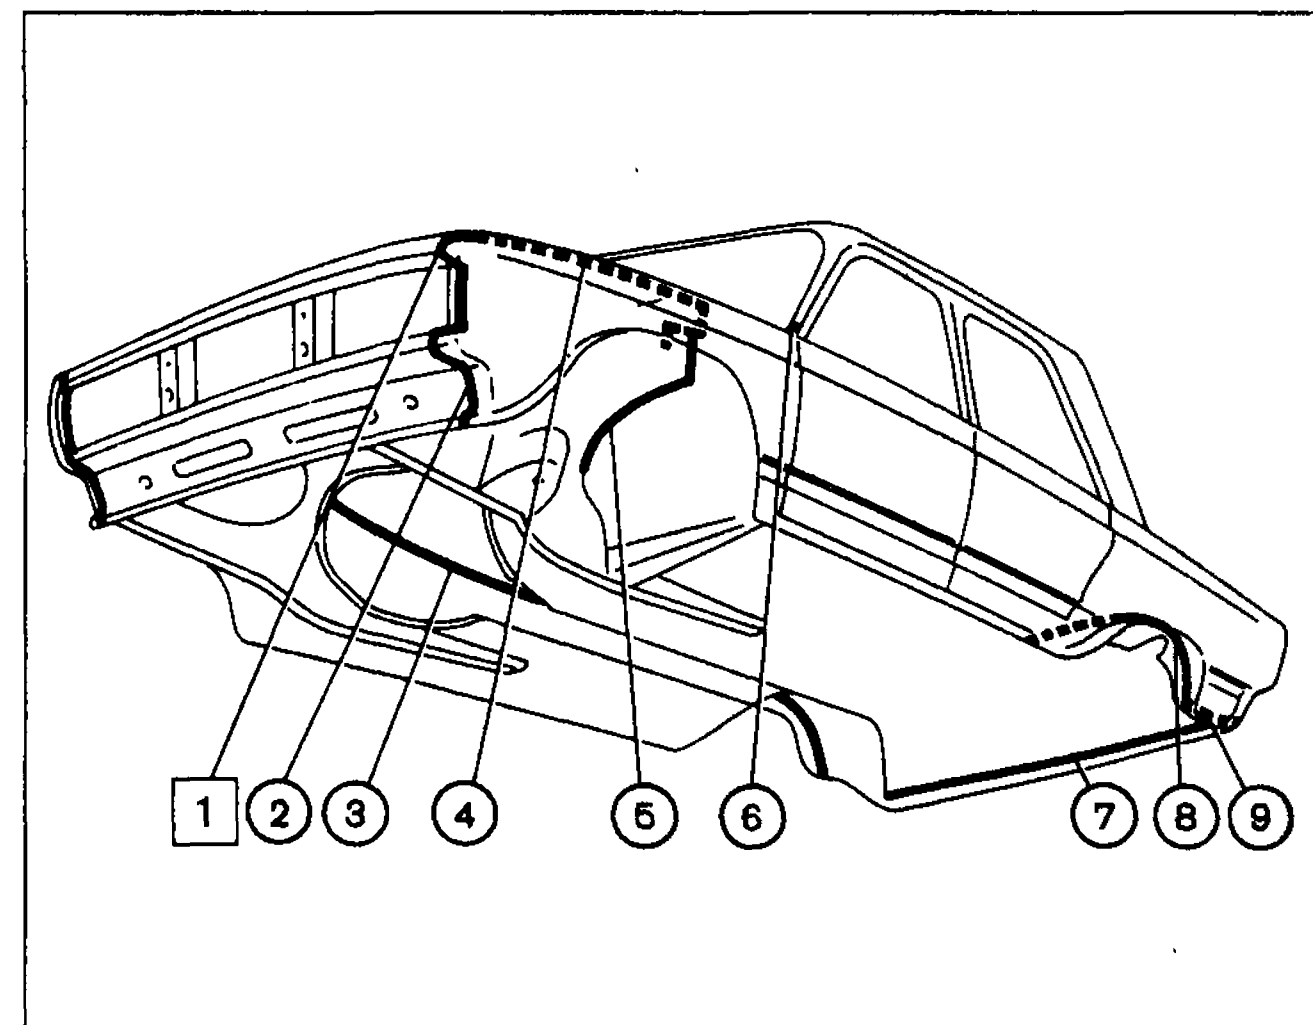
Сварные швы и стыки, на которые наносится уплотнительная мастика (вид кузова слева):
